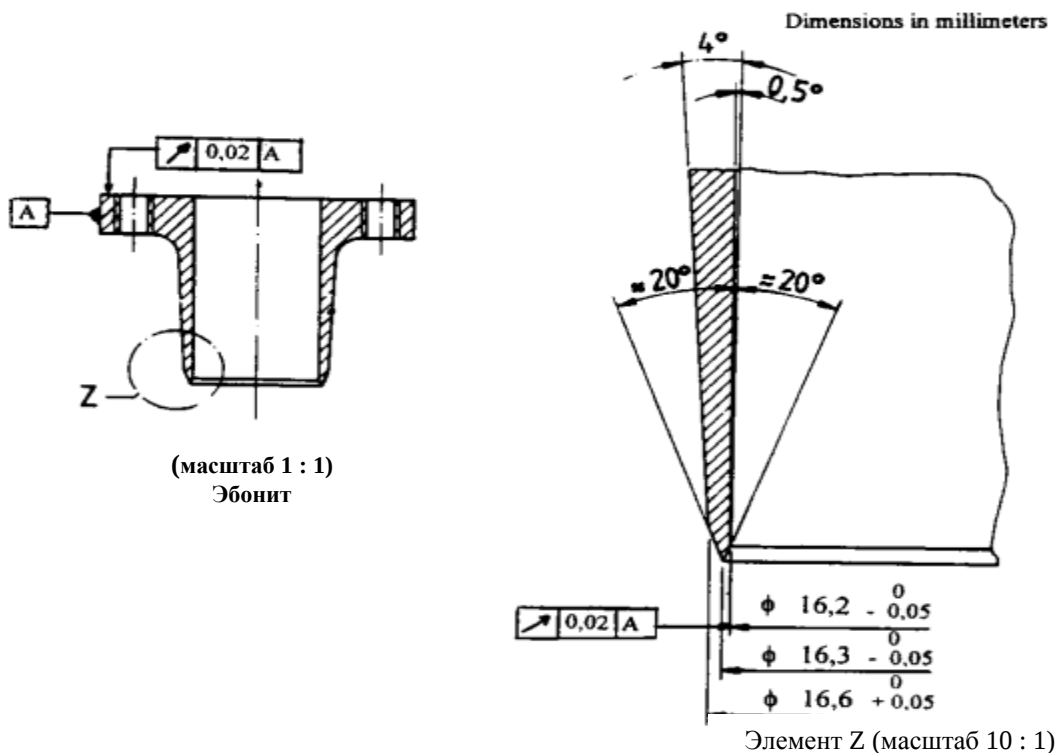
Ротационный вырубной штамп для приготовления испытываемых образцов
